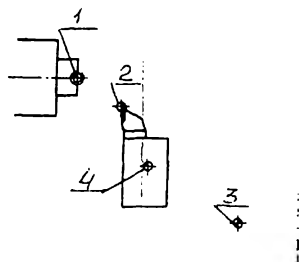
Схема автоматичного налагодження інструментів на токарному верстаті
